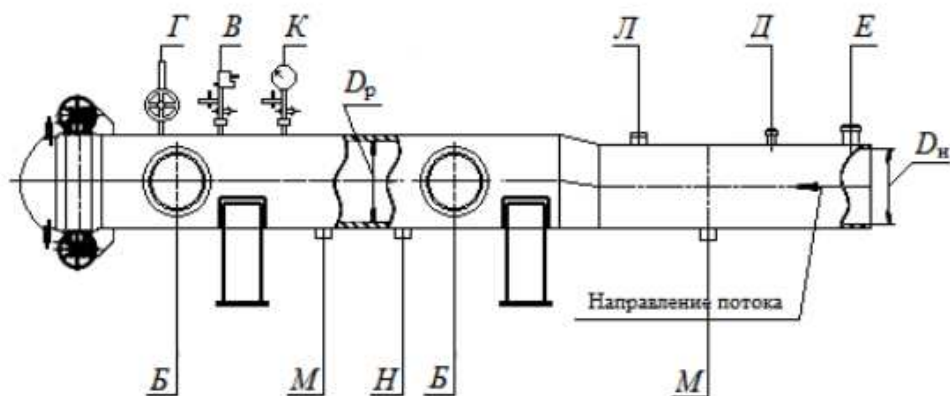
Камера приема СОД: Б – патрубки отвода продукта; В – патрубок для установки датчика давления; Г – патрубок для присоединения трубопровода газоз воздушной линии; Д – патрубок для подачи пара или инертного газа; Е – патрубок для установки сигнализатора рычажного; К – патрубок для установки манометра; Л – сигнализатор прохождения средств очистки и диагностики; М – патрубки для присоединения дренажных трубопроводов; Н – датчик контроля герметичности
